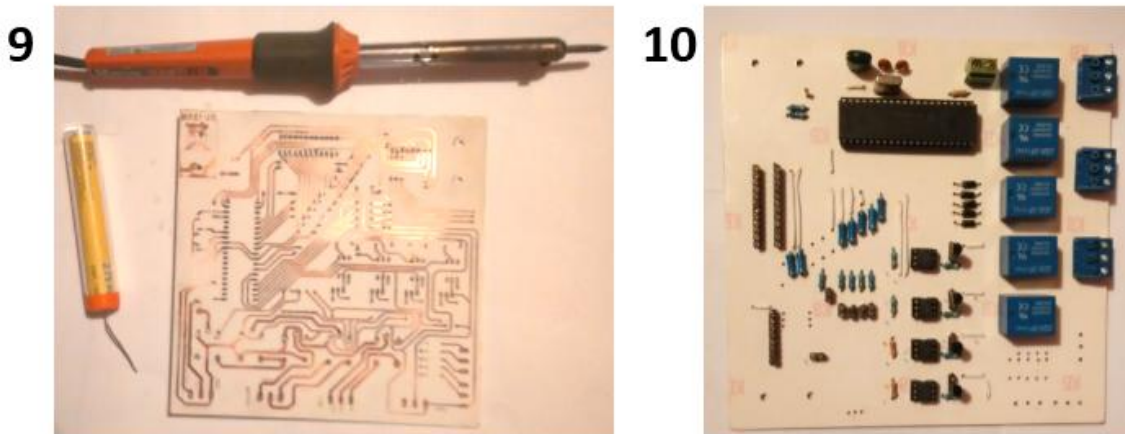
Pasos de la construcción del circuito electrónico: 9) Soldadura de los componentes y 10) Circuito electrónico terminado.
